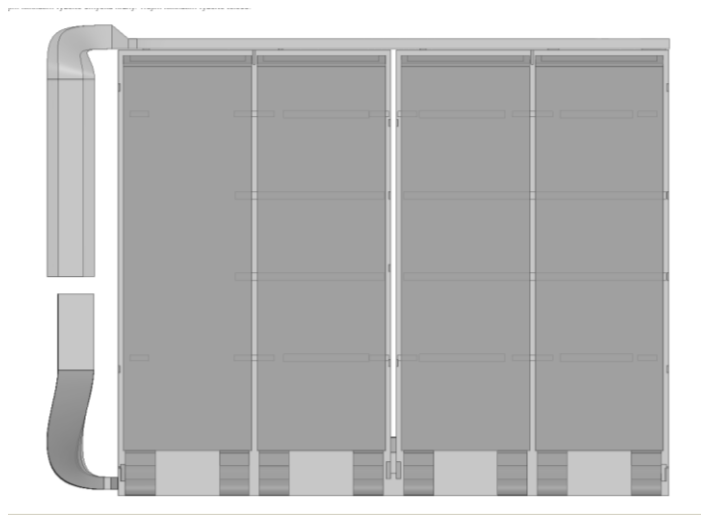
Úpravy geometrie 2 (vpravo na horní stěně původní geometrie jsou zřejmé pevnostní prvky a mřížky, které byly v rámci zjednodušení odebrány)
